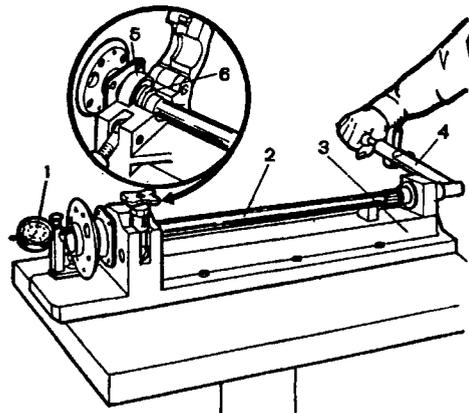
Проверка усилия, с которым выпрессовывается запорное кольцо подшипника полуоси, с помощью приспособления А.95601/Р и динамометрического ключа: 1 - индикатор; 2 - полуось; 3 - приспособление А.95601/Р; 4 - динамометрический ключ; 5 - шарикоподшипник; 6 - запорное кольцо подшипника
